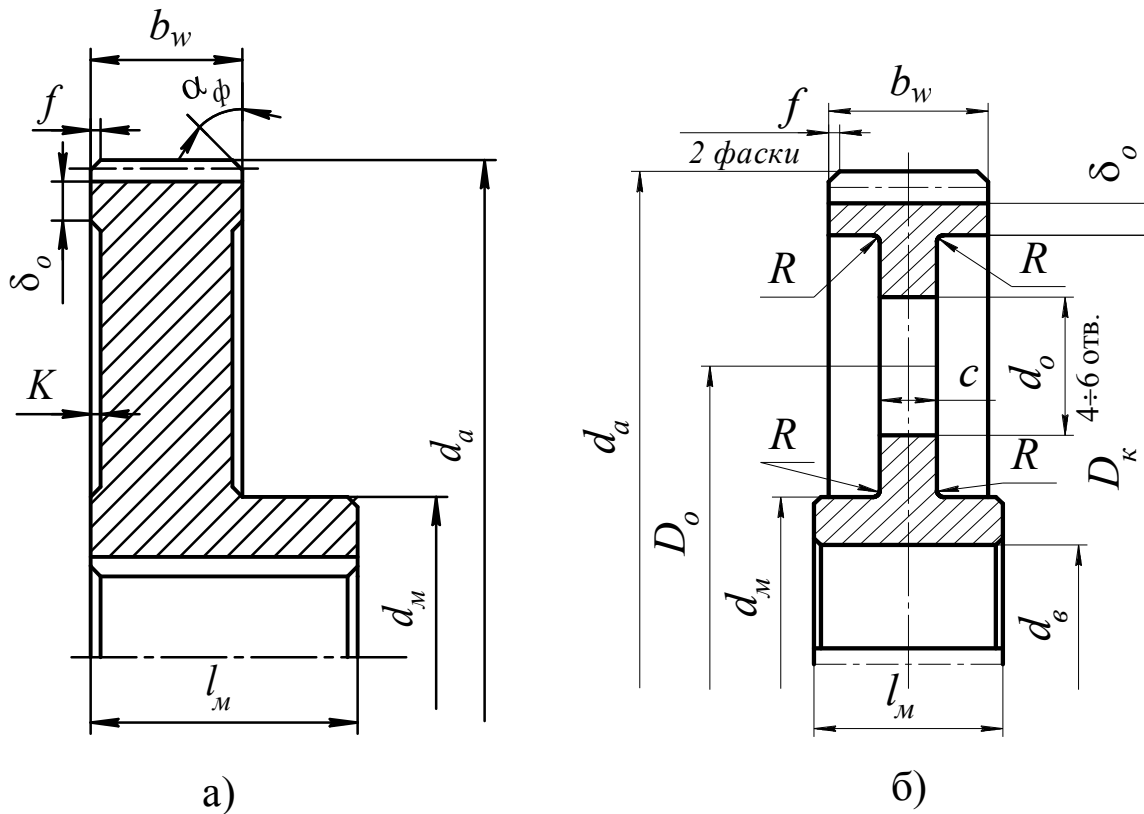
Конструкция штампованного (кованого) цилиндрического зубчатого колеса
